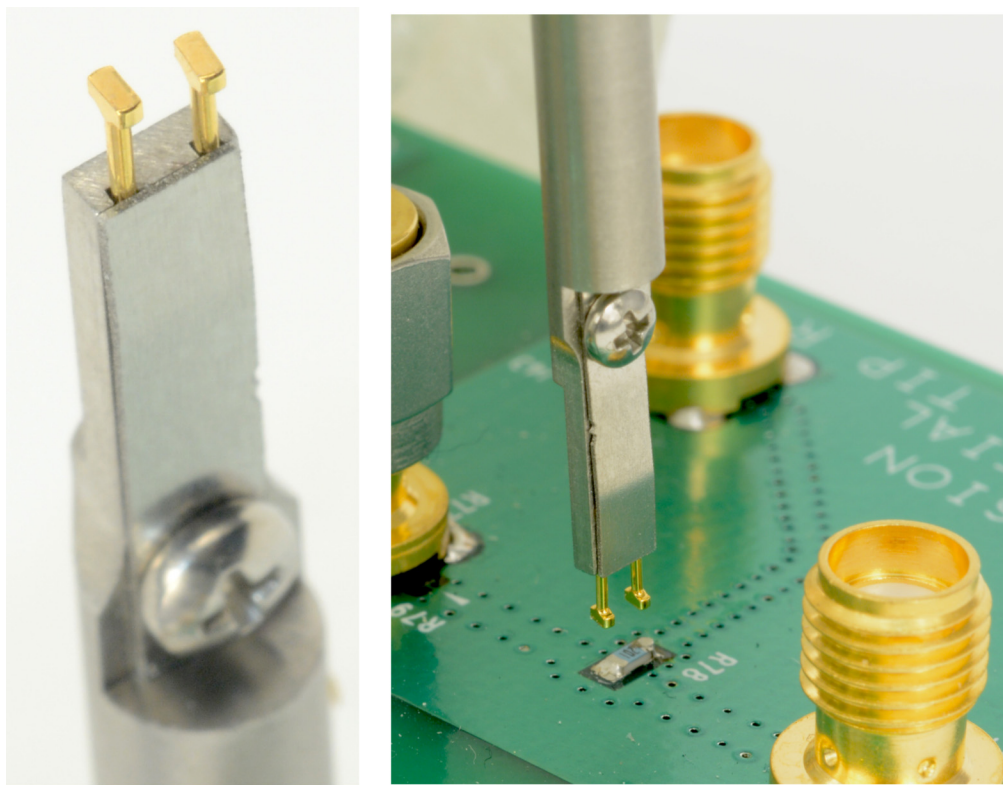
Использование вспомогательного приспособления для установки штырей квадратного сечения на печатной плате.
